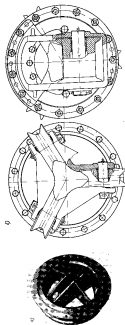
Автоматический ящик: а — с лентой чулковой; б — с лентой стальной
